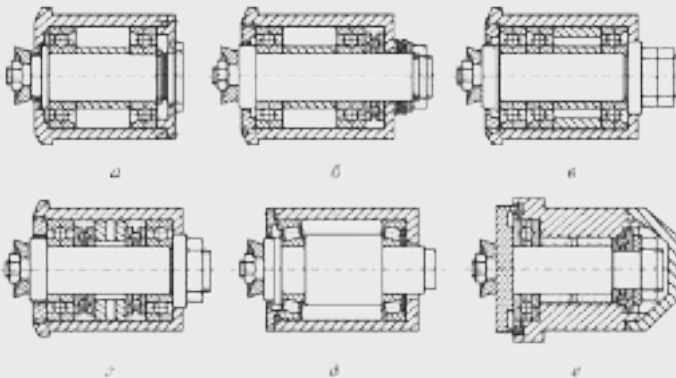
Конструкція ротаційних різців на підшипниках кочення: а — радіально-упорні; б — два радіальних підшипники; в — спарені підшипники; г — два упорних підшипники; д — конічні роликові підшипники; е — упорні кулькові підшипники
